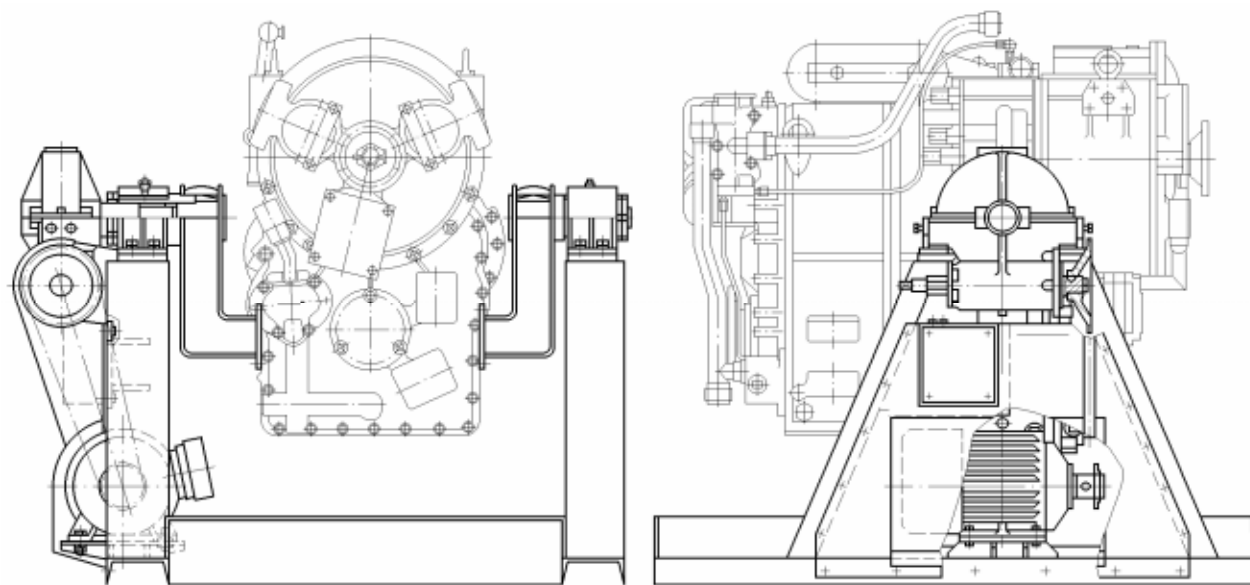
Стенд для разборки и сборки гидромеханической передачи
